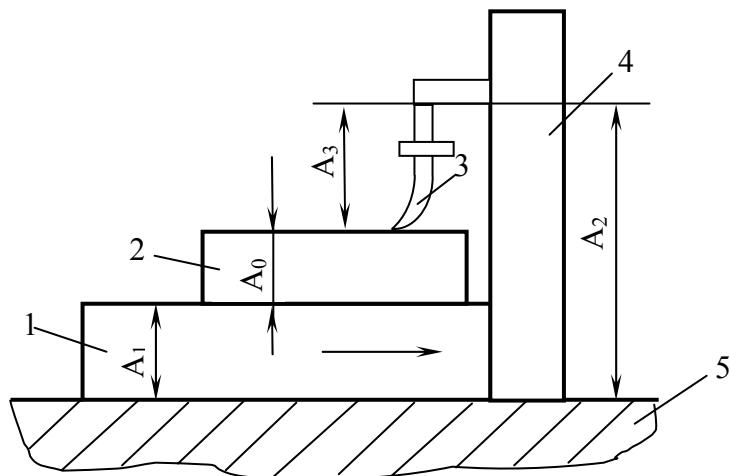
Включение обрабатываемой детали в размерную часть строгального станка: 1 – стол; 2 – деталь; 3 – резец; 4 – суппорт; 5 – станина [26]
